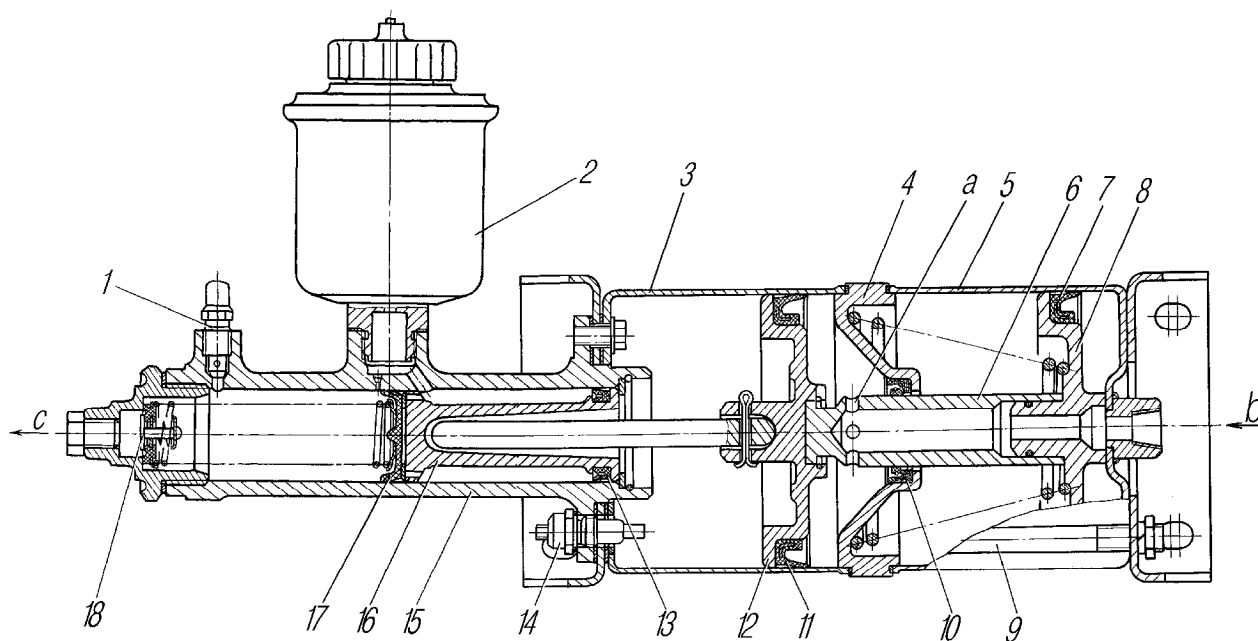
Усилитель пневматический с главным тормозным цилиндром: 1- клапан перепускной; 2- бачок для тормозной жидкости; 3,5- пневмоцилиндры; 4- проставка; 6- шток; 7,10,11,13,17- манжеты; 8,12,16- поршни; 9- стяжка; 14- включатель сигнализатора неисправности тормозов; 15- цилиндр тормозной главный; 18- клапан обратный; а- радиальное отверстие; б- от тормозного крана; с- в тормозную систему
